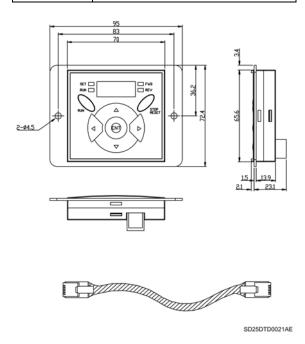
Unidad de teclado / display remoto y cable remoto
